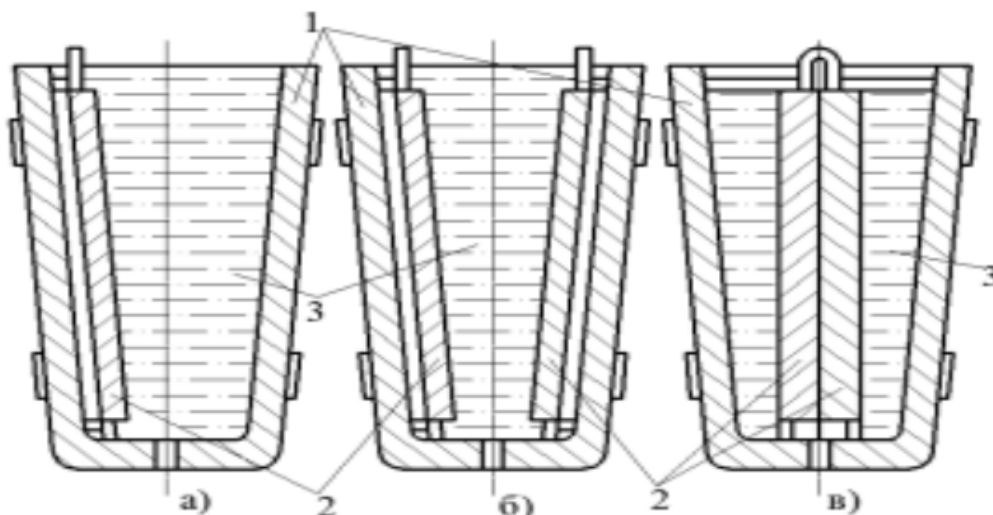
Виробництво біметалів заливкою: а) одношаровий біметал; б) двошаровий біметал; в) тришаровий біметал. 1- виливниці; 2 - твердий шар металу; 3 - рідкий метал.
